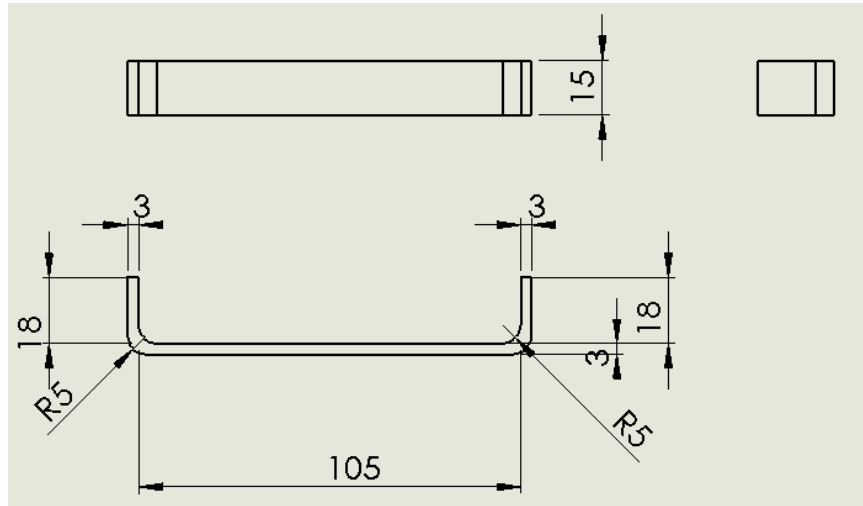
Plano Ángulos Sujetadores de Baterías (mm).
